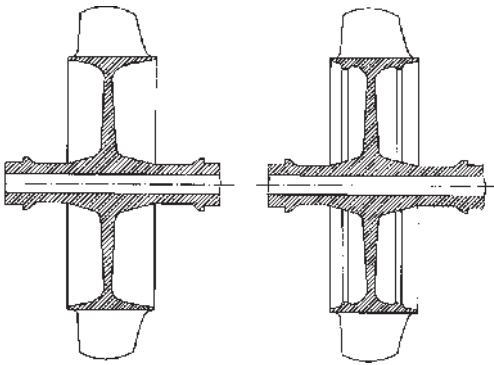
Älteres, bewährtes Verdichterrad (links); nach Andrehen zweier Wuchtringe anfälliges Verdichterrad (rechts).
